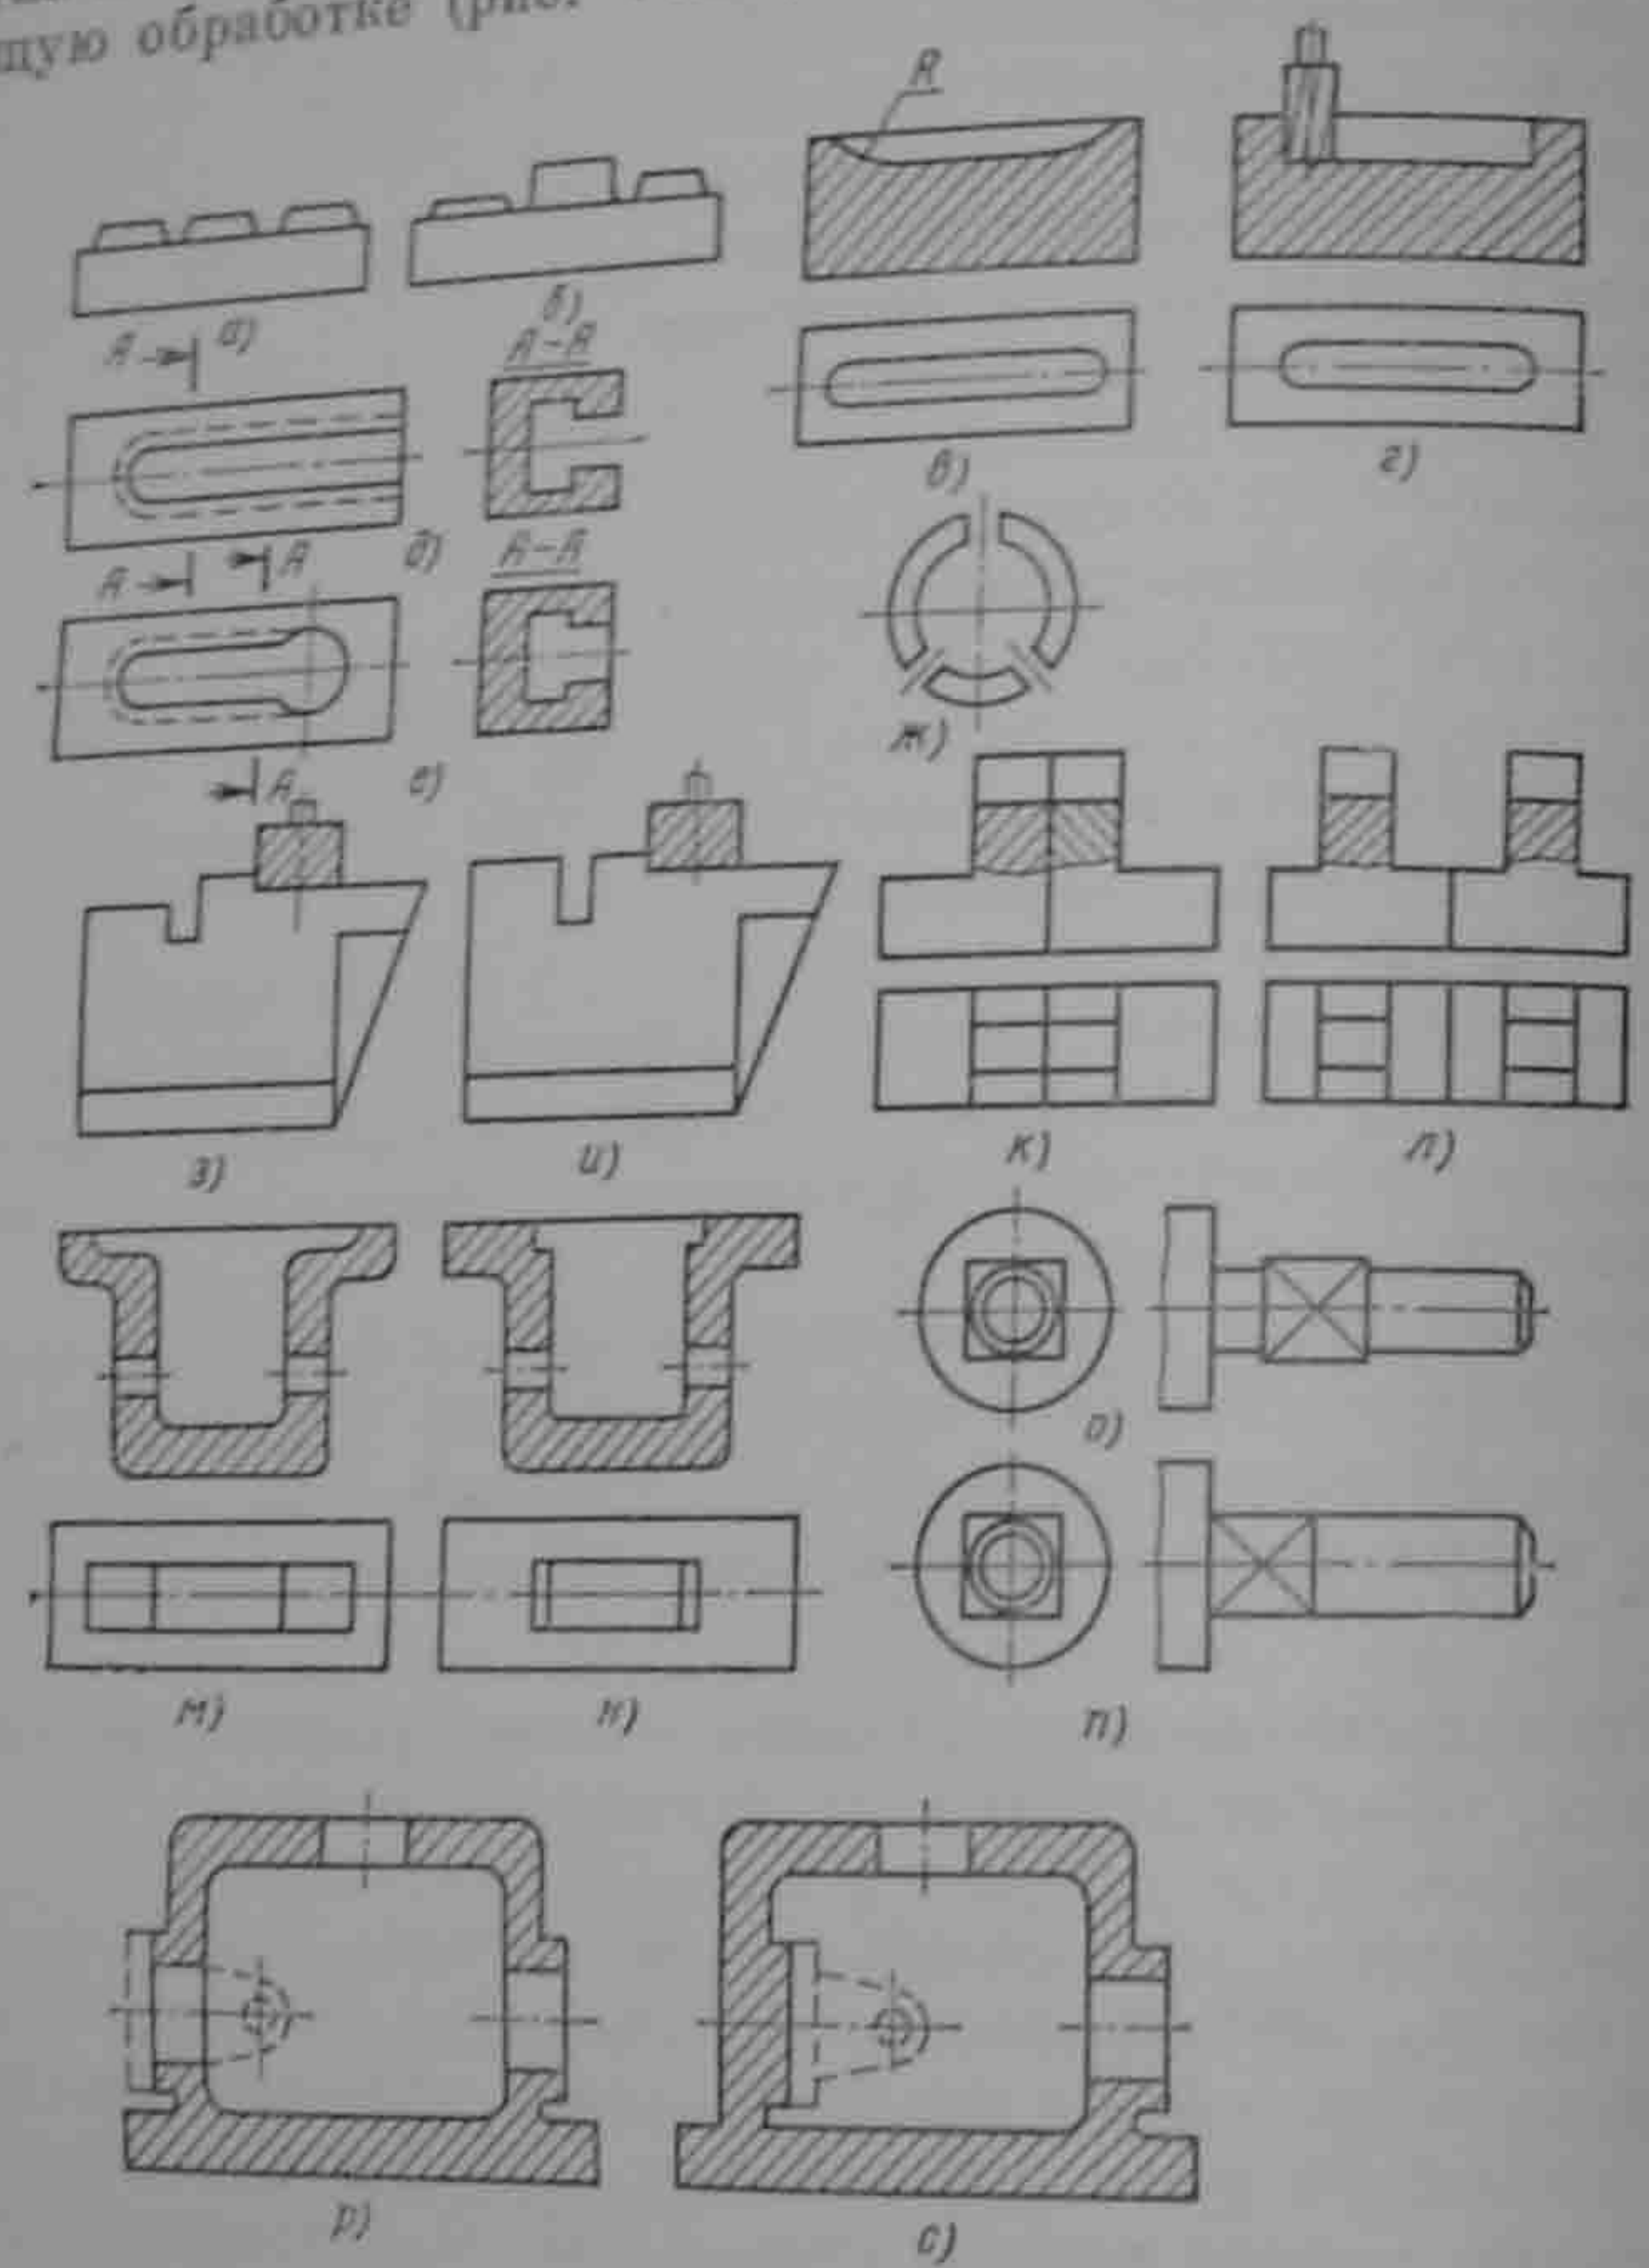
Примеры конструкций деталей машин, обрабатываемых на фрезерных станках
